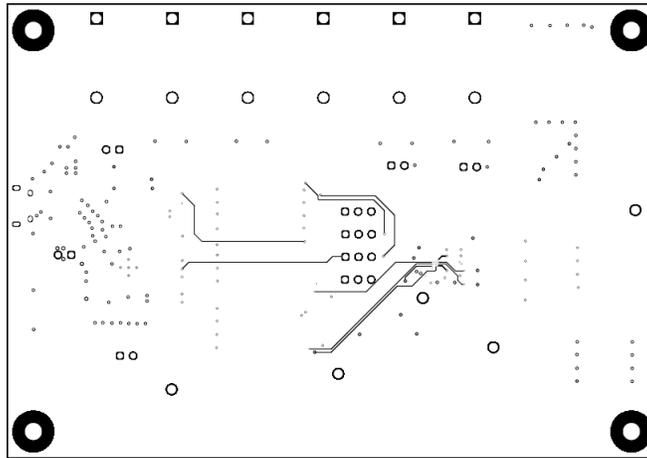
AMC6V704EVM PCB 中层 3 布局 (信号层)
